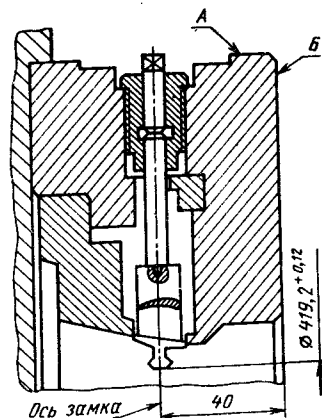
Схема установки и закрепления рабочей лопатки компрессора в приспособлении для точения кольцевого трапецевидного хвостовика
